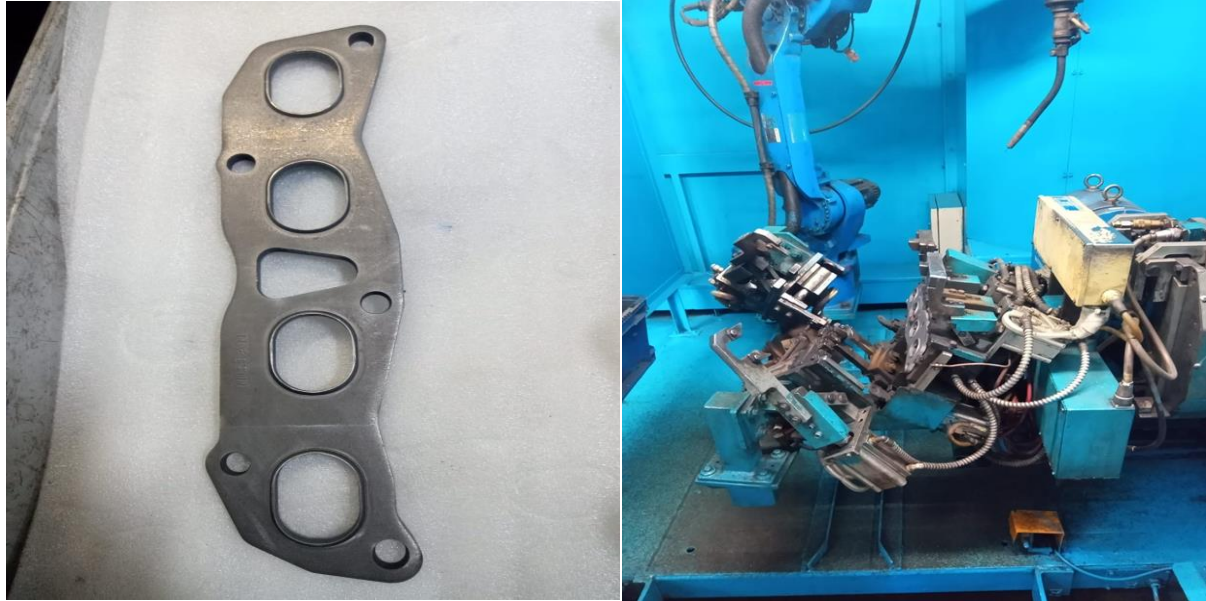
Imágenes referentes a la cabina #1 (lado B) de soldadura.
